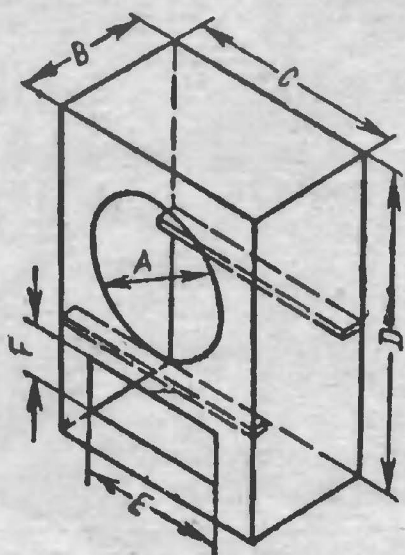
Устройство фазоинвертора для громкоговорителя.
